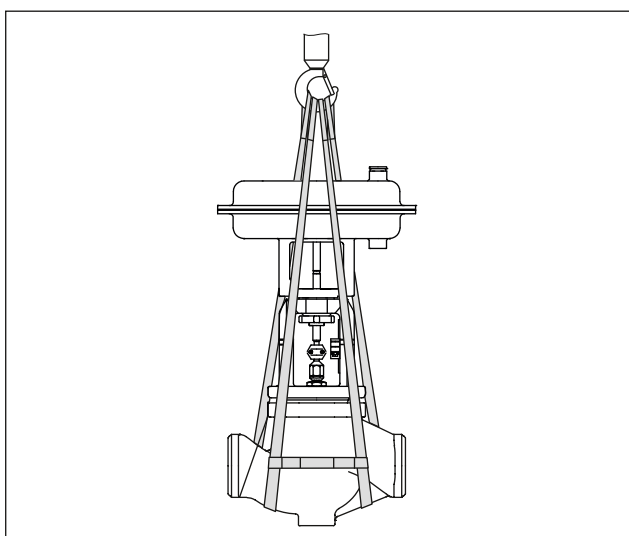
Подъем регулирующего клапана с патрубками под приварку (примерное изображение): подъемные петли, размещённые на корпусе, должны быть скреплены друг с другом с помощью соединительного устройства, чтобы предотвратить их соскальзывание.
